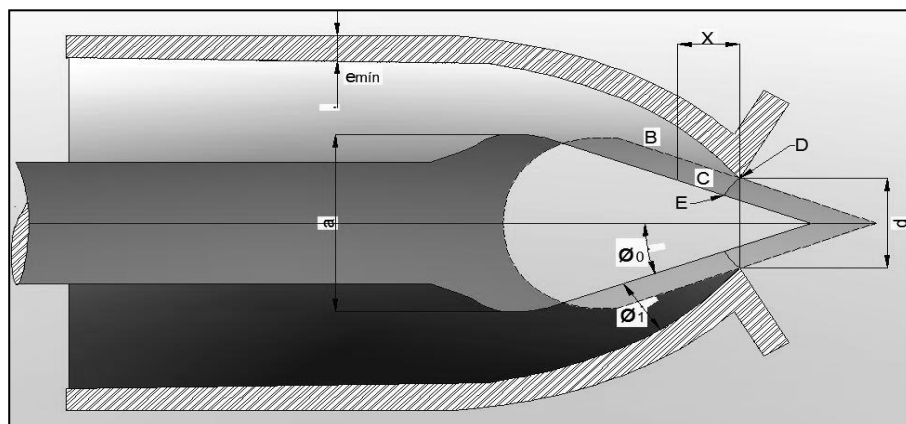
Dimensiones de un inyector de una turbina Pelton. [9]
